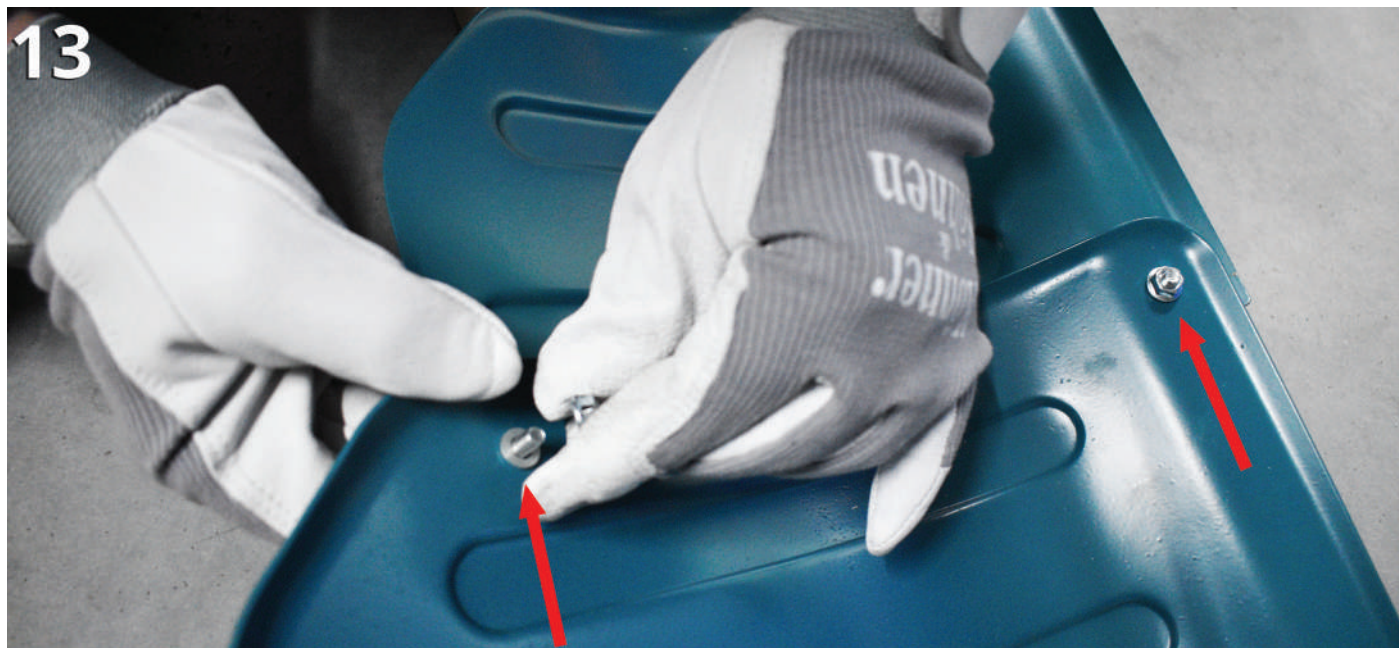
Befestigen Sie die Kotflügel mit Schrauben am Körper des Bodenhackens.
